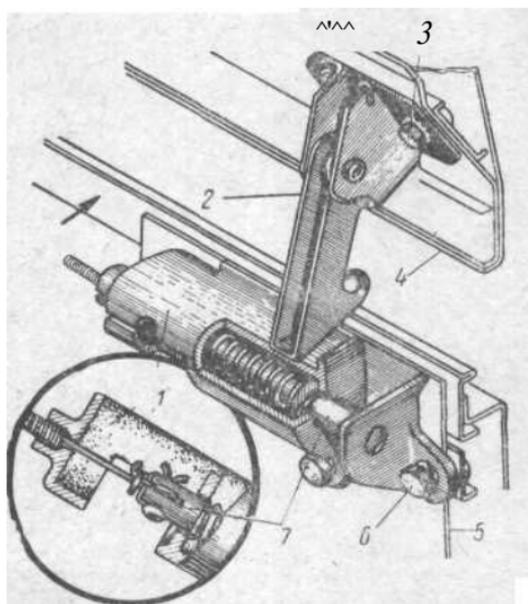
Механизм запора багажника: 1 — корпус запора; 2 — крючок (защелка); 3 и 6 — болты; 4 — крышка багажника; 5 — пружина; 7 — стержень запора
